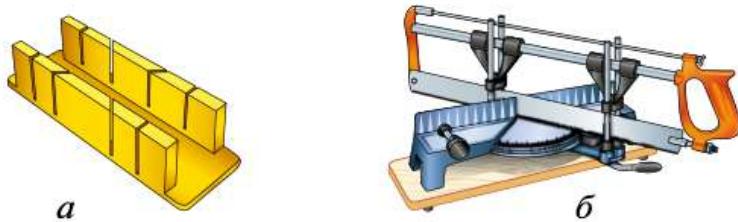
Приспособления для точного пиления заготовок из древесины: *а* — стусло П-образное; *б* — стусло поворотное
